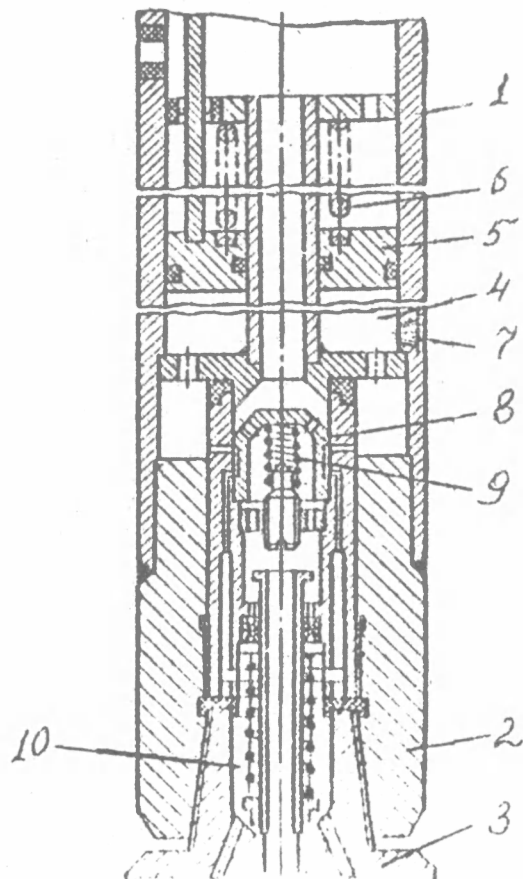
Наддолотный лубрикатор для смазки опор шарошек
